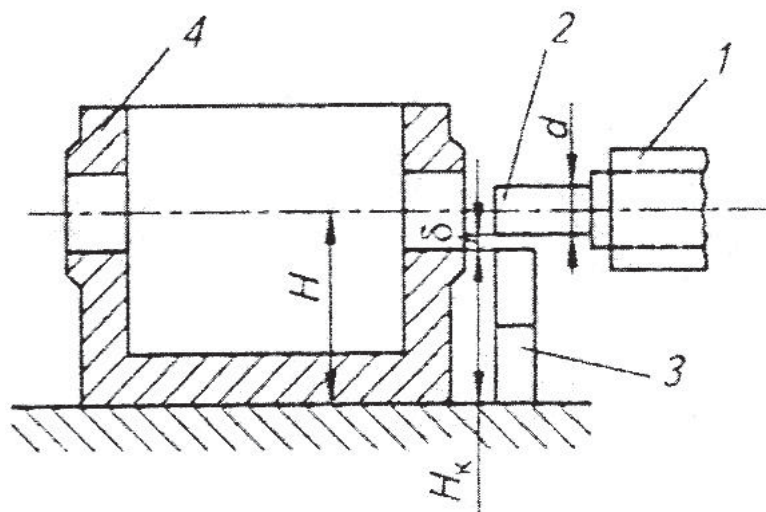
Схема расточки отверстий корпусной с использованием мерной оправки и концевых мер: 1 – шпиндель; 2 – мерная оправка; 3 – концевые меры; 4 – деталь
